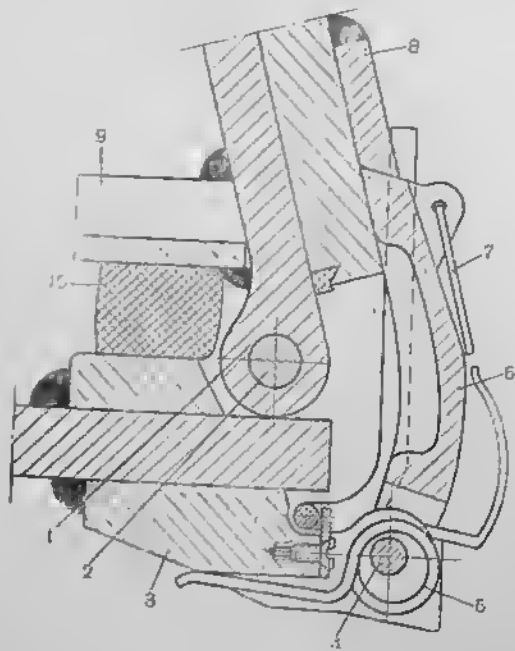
Петля крышки командирской башенки со специальным стопором:
